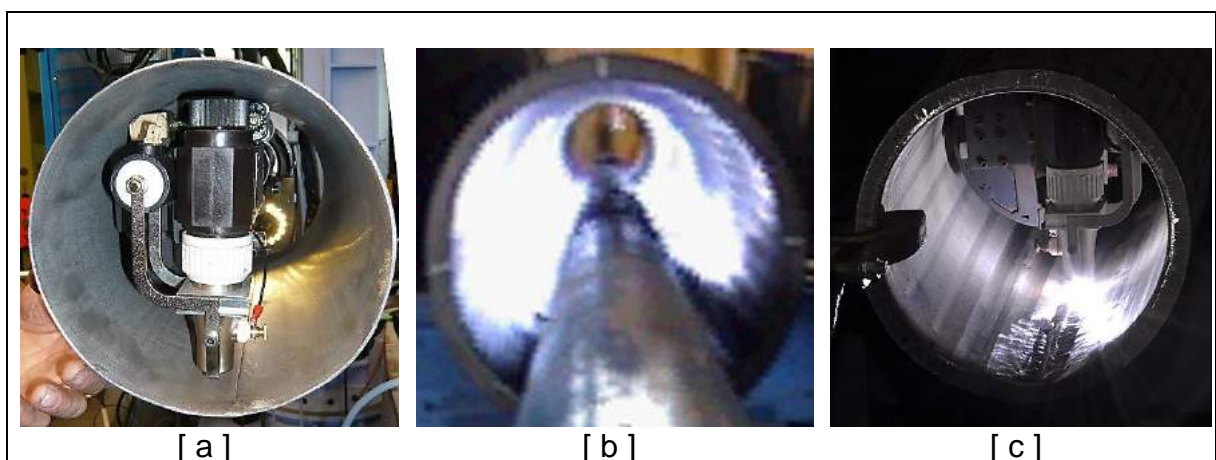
Equipamento de soldagem: [a] vista frontal da montagem; [b] visão posterior da soldagem, a partir da lança de sustentação; [c] vista frontal da soldagem.
